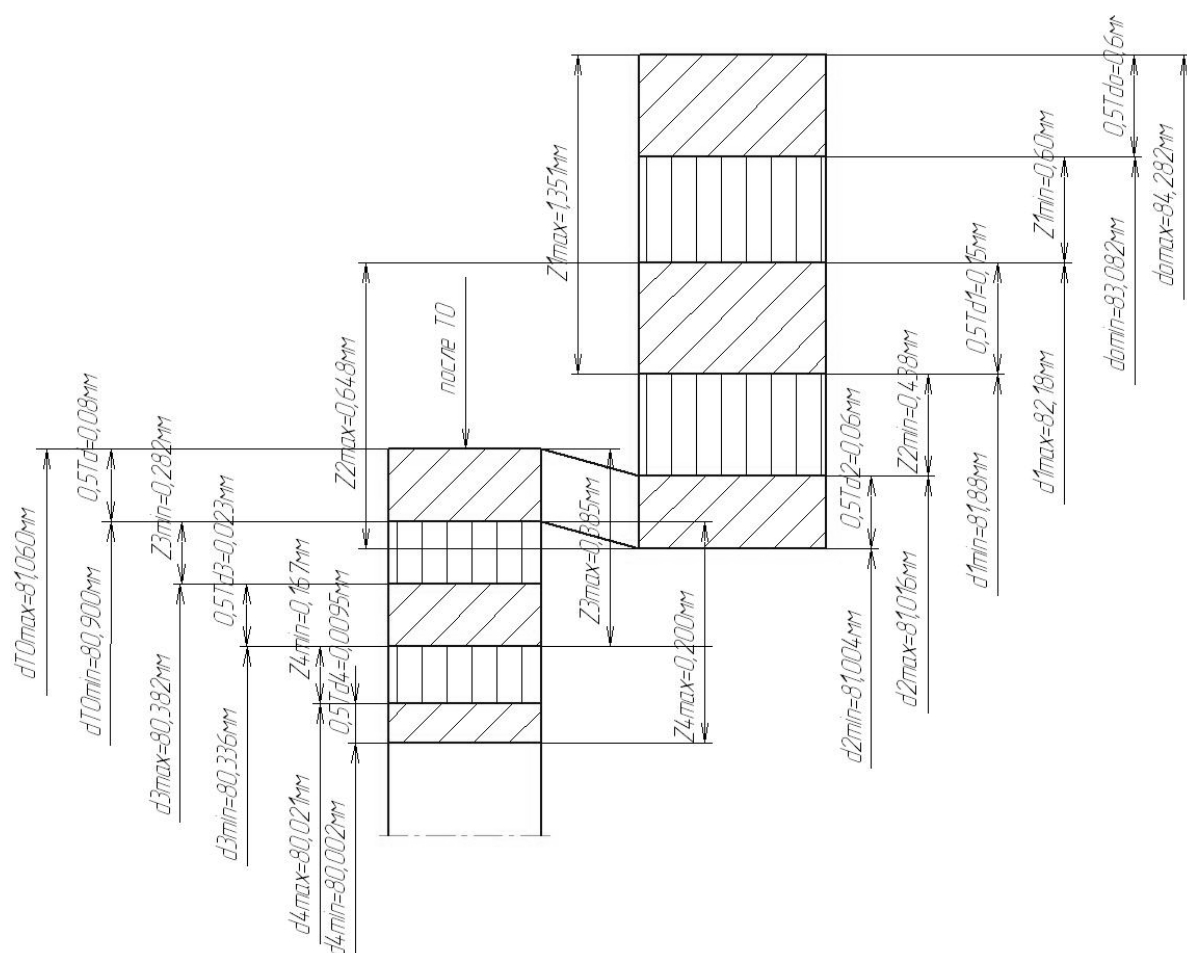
Схема расположения припусков и допусков
